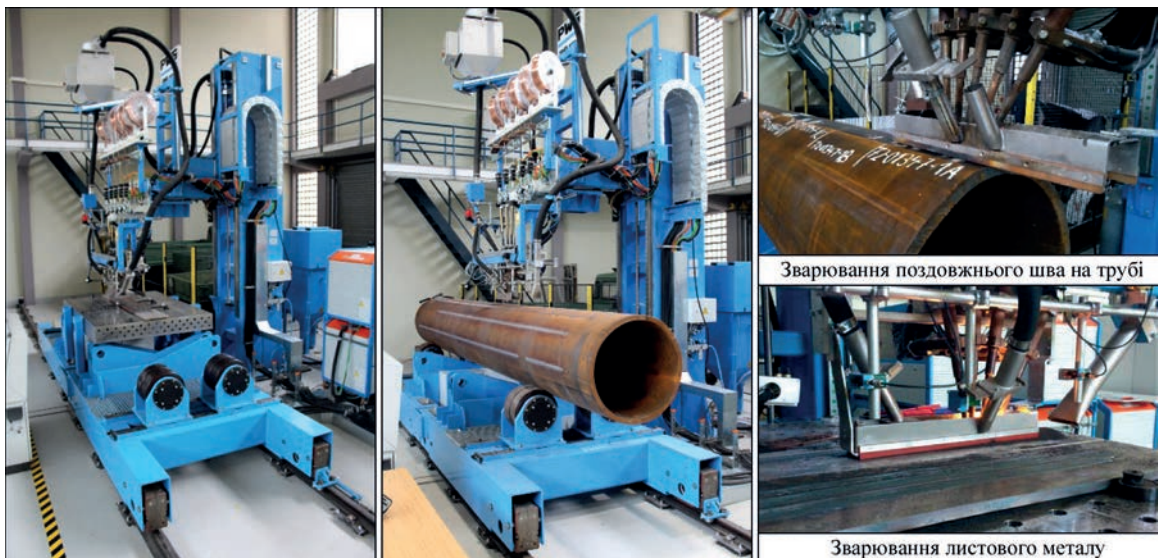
П'ятидротяний стенд для зварювання листів і труб у Fraunhofer IPK у Берліні
